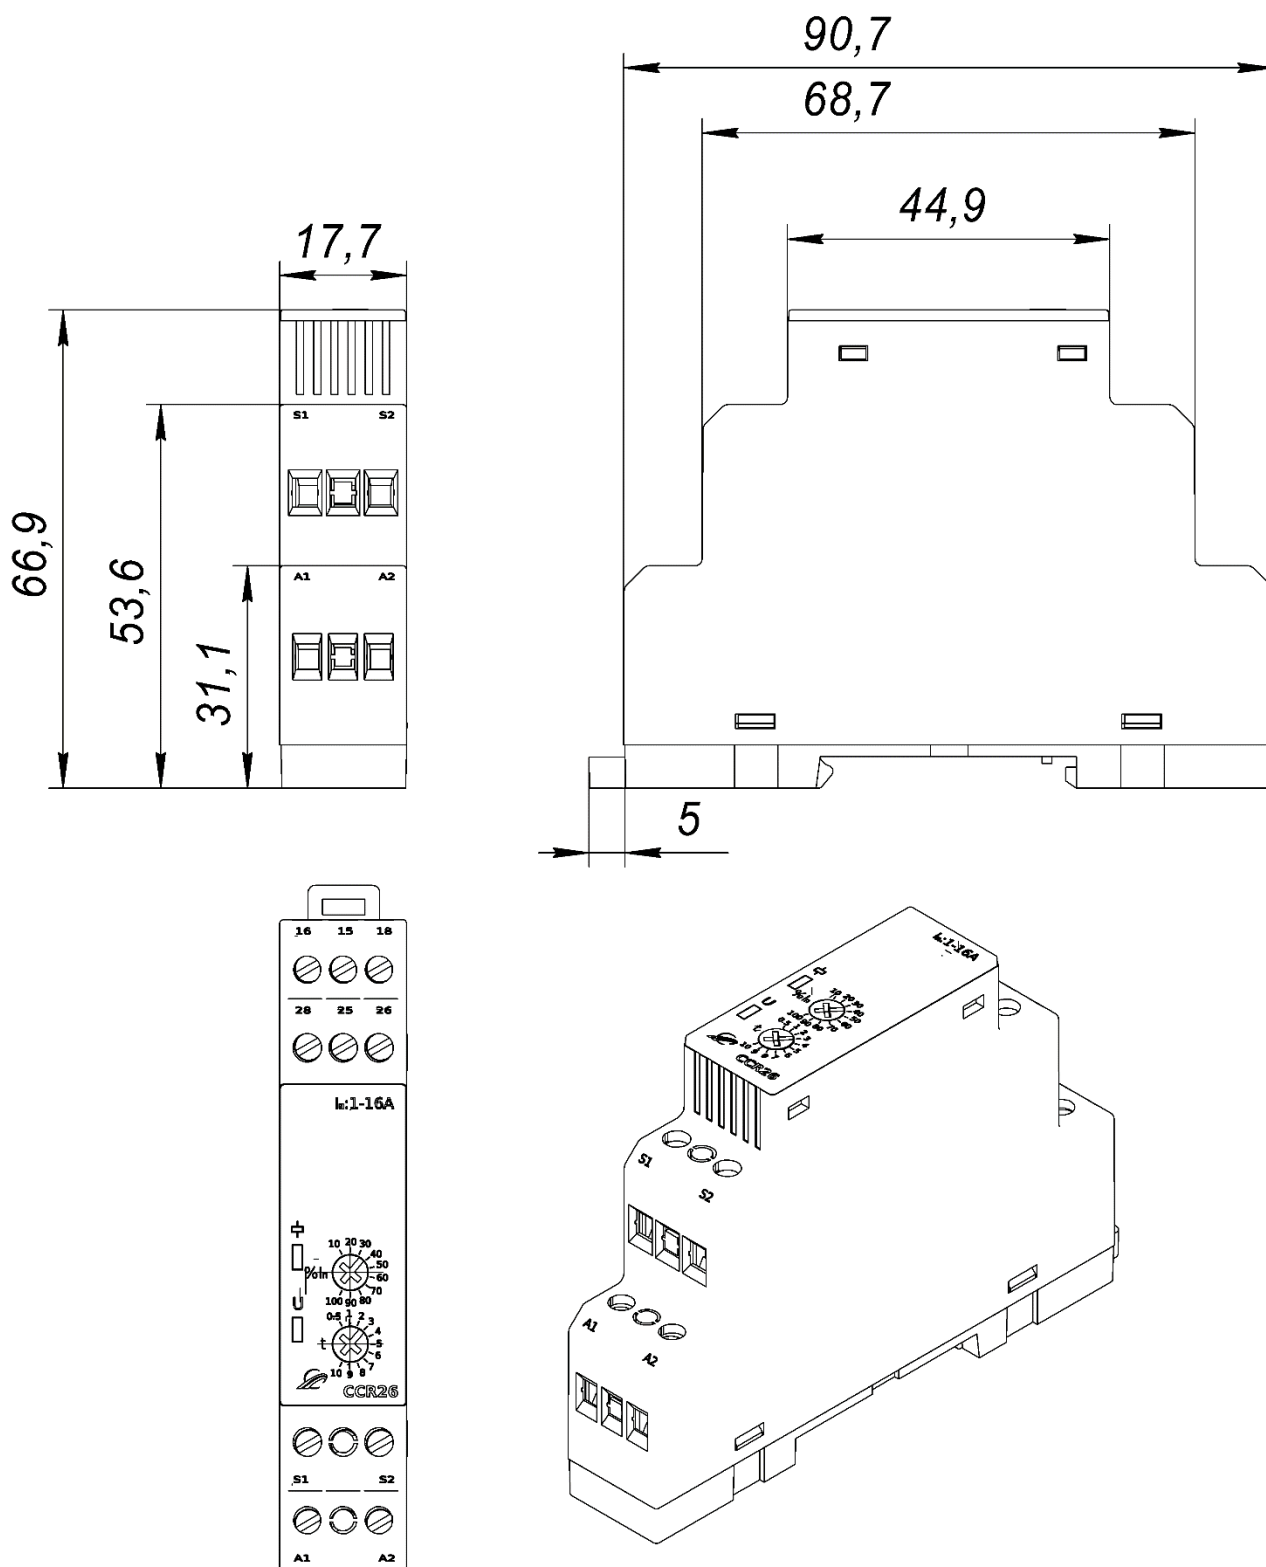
Габаритные размеры реле контроля тока CCR26
